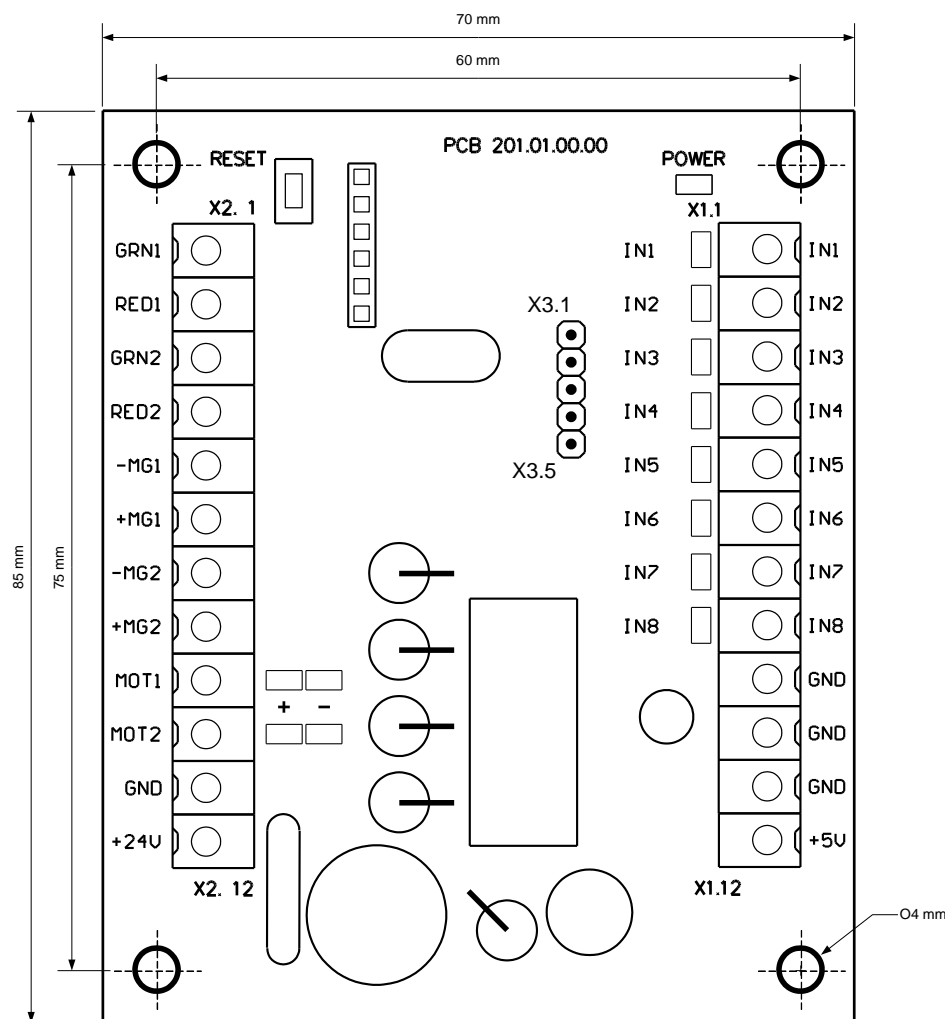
Внешний вид контроллера PCB.201.01.00.00
